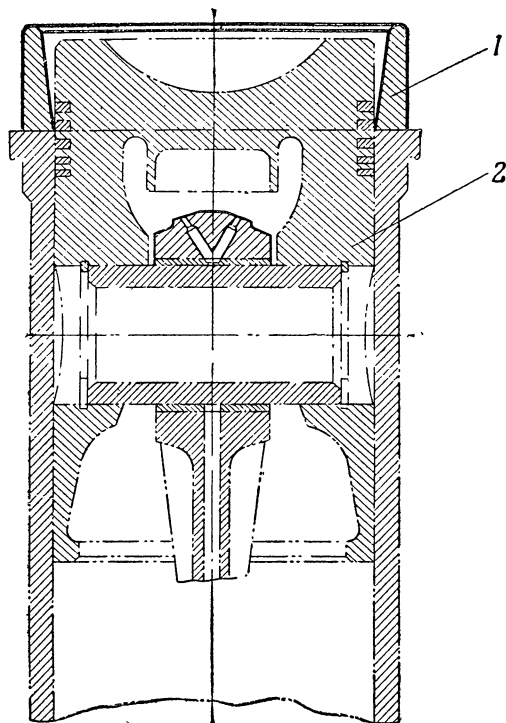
Установка поршня с кольцами и шатуном в цилиндр:
